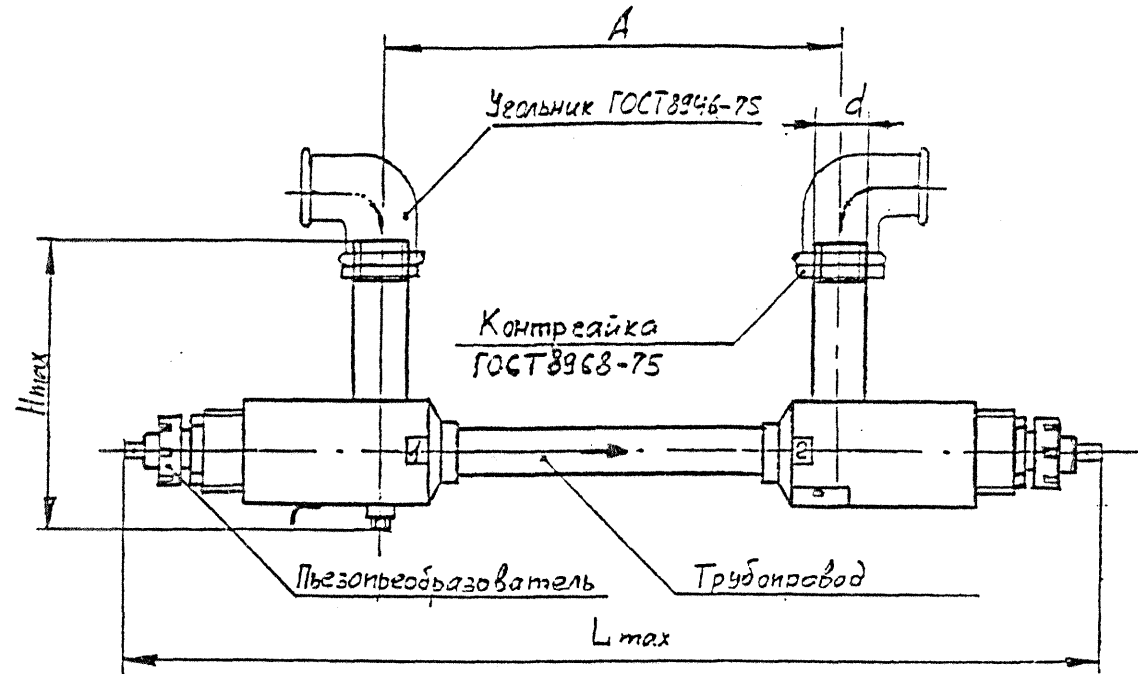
Преобразователь первичный ПП14. Общий вид
